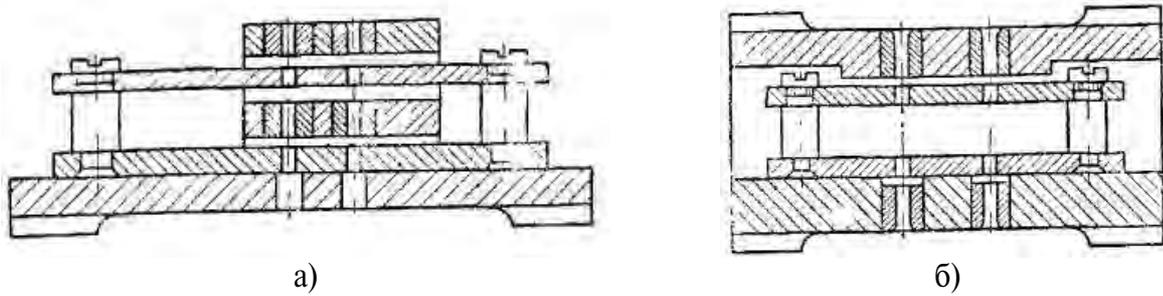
Кондуктор для сверления платинок в собранном виде:
